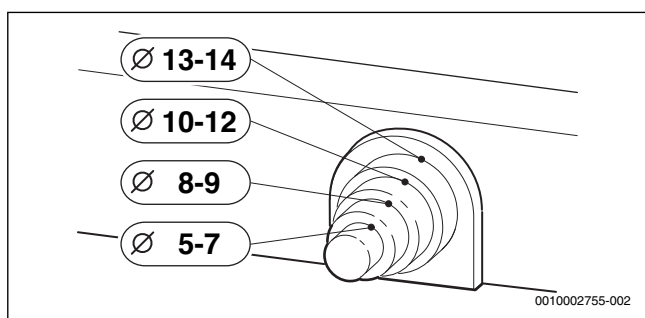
Zugentlastung an Kabeldurchmesser anpassen
